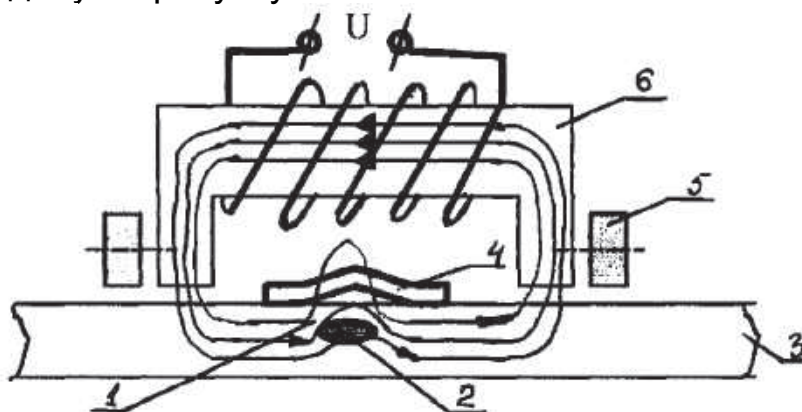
Схема намагнічування зварного шва разом із магнітною стрічкою
